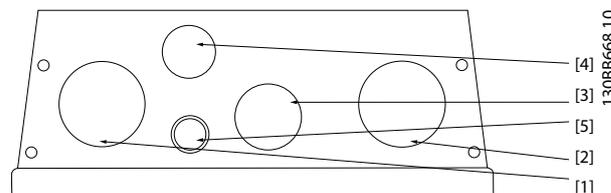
Baugröße B1, IP55 Kabeleinführungsöffnungen mit metrischem Gewinde
